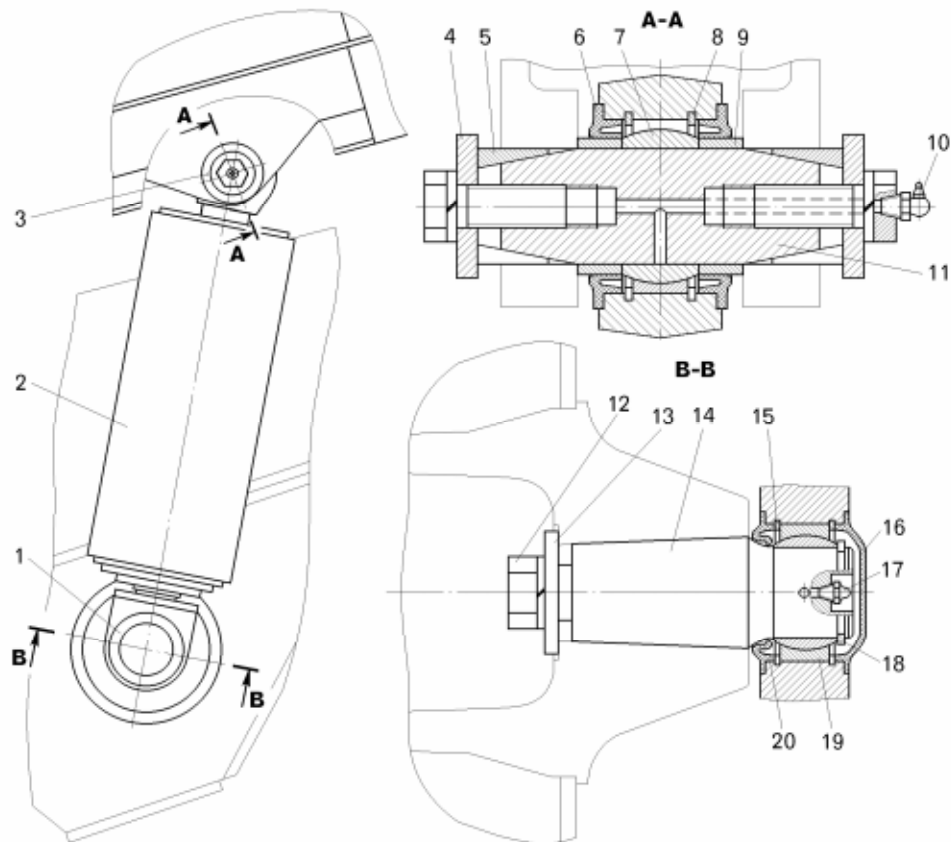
Гидроцилиндр опрокидывающего механизма
